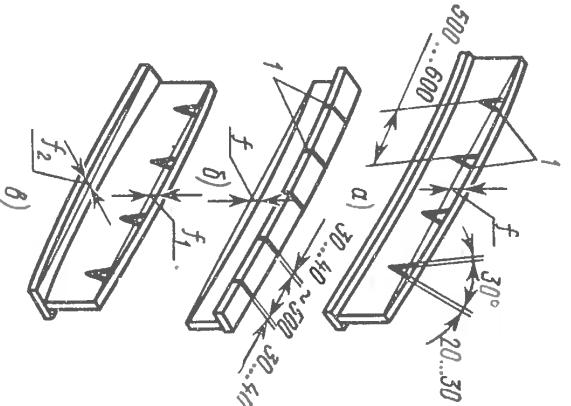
Схемы термической правки балок таврового сечения нагревом верхней части вертикальной стенки (а), нагревом пояса (б) и нагревом вертикальной стеки и пояса (в);
